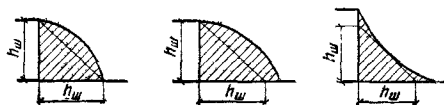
Схема сечений сварных угловых швов
